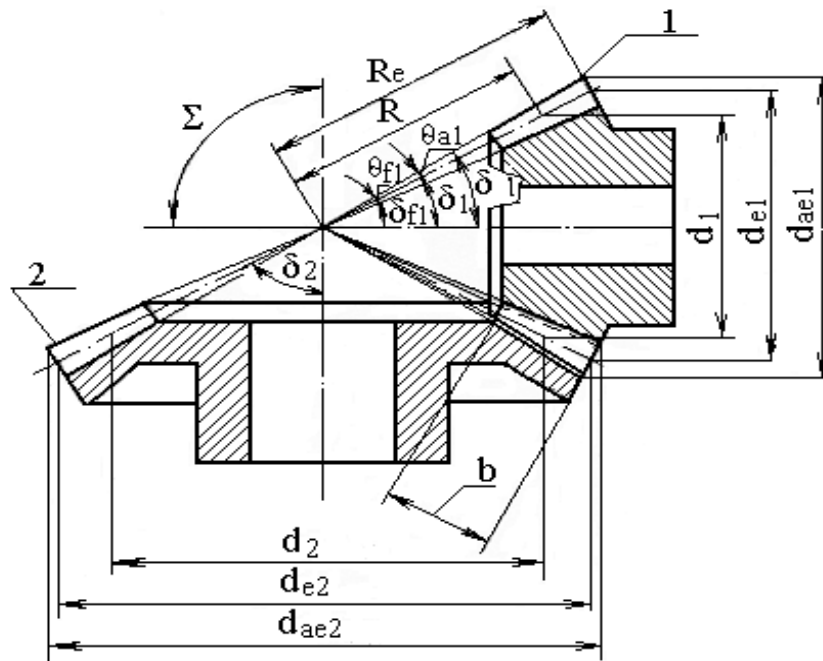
Передача коническая: 1 – колесо ведущее; 2 – колесо ведомое
